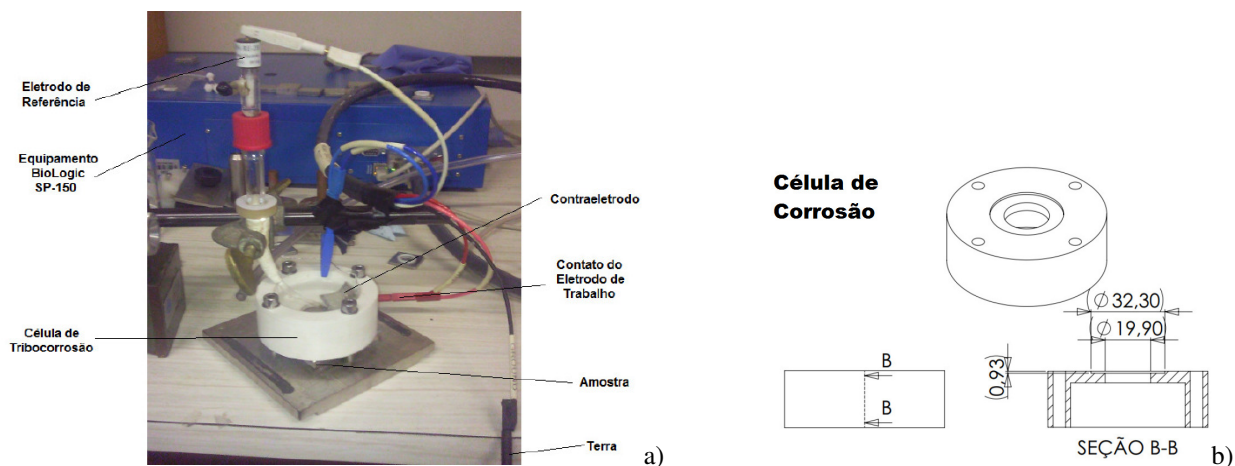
a) Montagem do conjunto para os testes de corrosão. b) Projeto da Célula de Corrosão.
